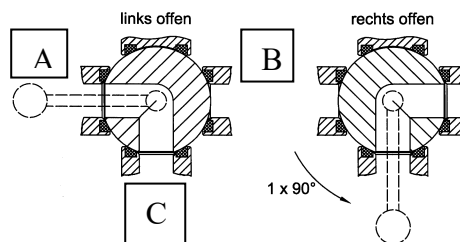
3-Wege-Kugelhahn L-Bohrung mit vollem Durchgang und Flanschanschluss nach DIN EN 1092-1 Form B1; Baulänge: Grundreihe 28 nach DIN EN 558-1 (F17 nach DIN 3202 Teil 1)
